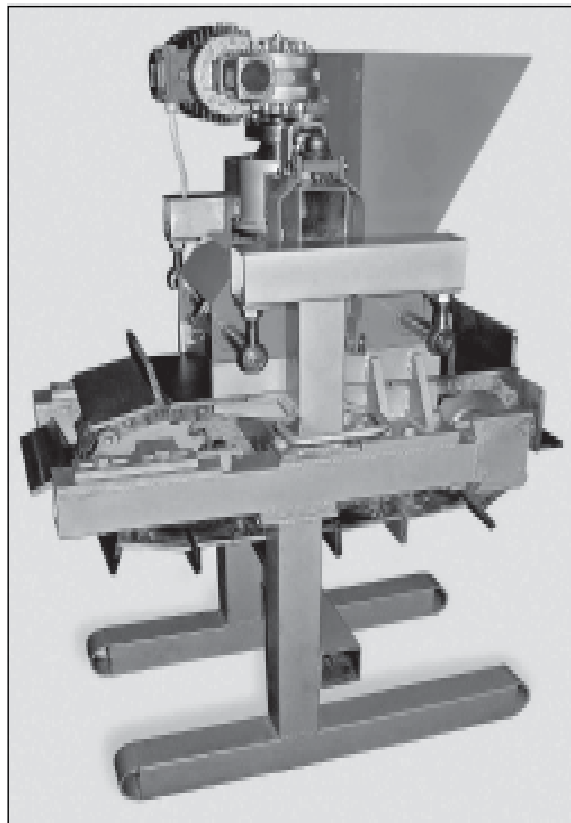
Опытный образец формовочной машины «РК\_мини\_01»
